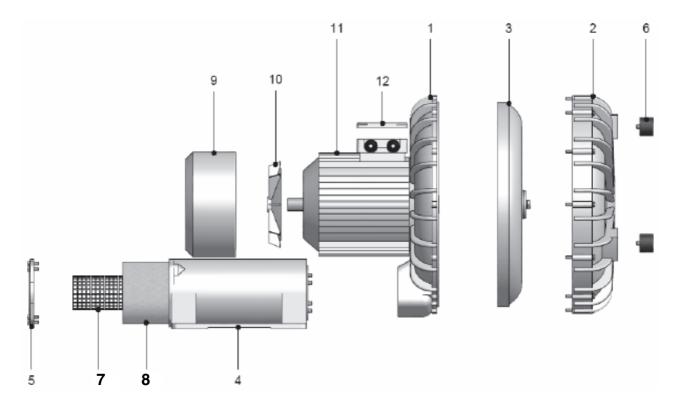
Схема-разброска (из инструкции изготовителя)
